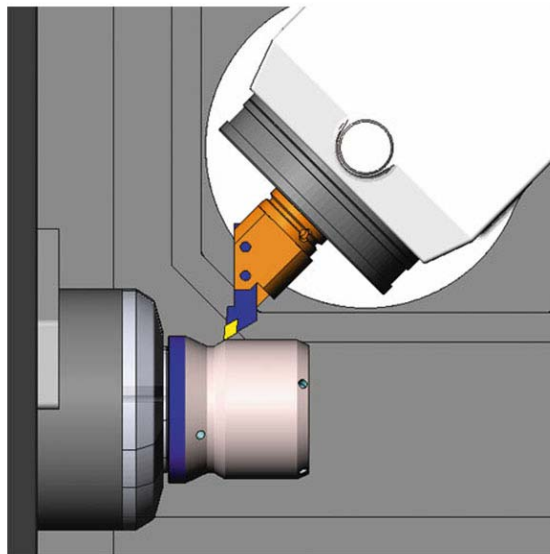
Универсальность крепления токарного и фрезерного инструмента в голове с осью В
